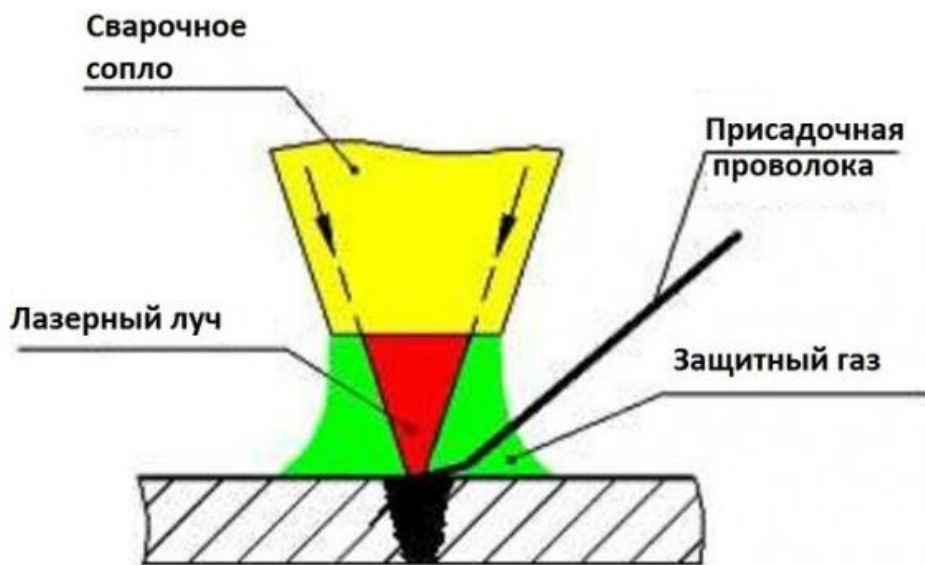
Схема выполнения лазерной сварки
